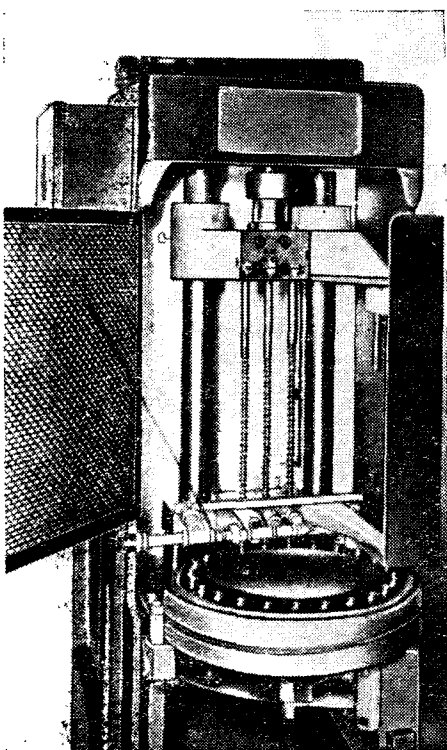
Вертикально-протяжной трехпозиционный станок с автоматическим поворотным столом
